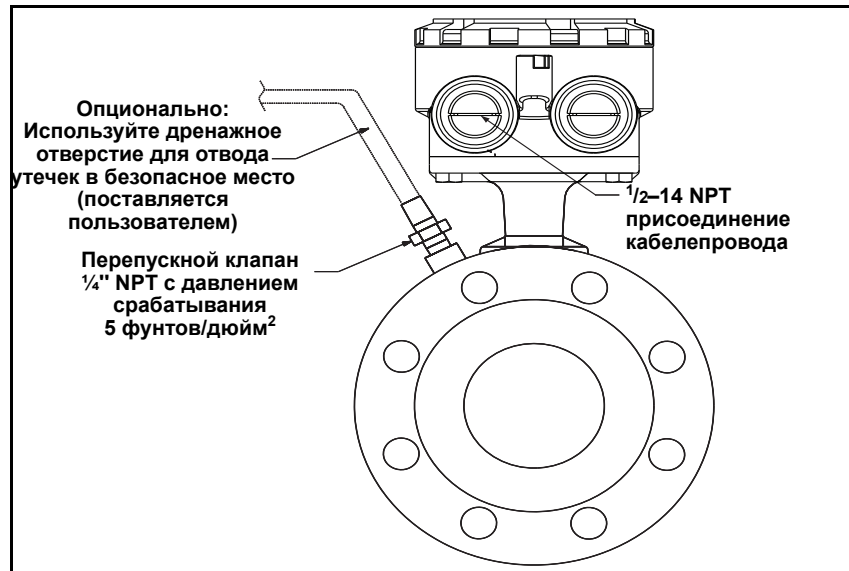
Стандартное исполнение корпуса — герметичный сварной корпус (код W0).
